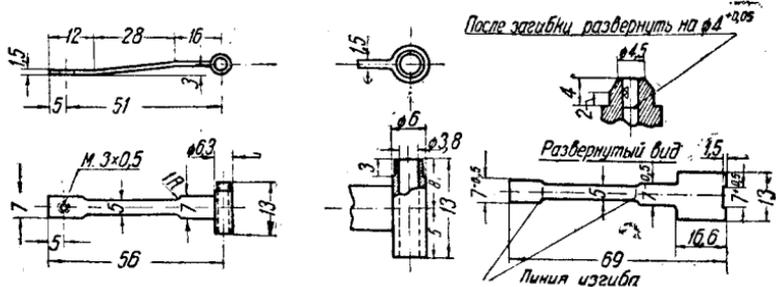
Дет. № 324. Рычаг поплавка для топлива
